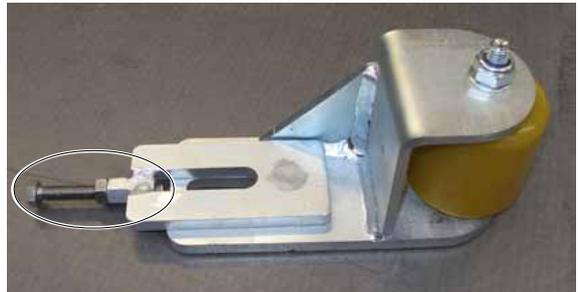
Andruckrolle, Einstellschraube mit Kontermutter
